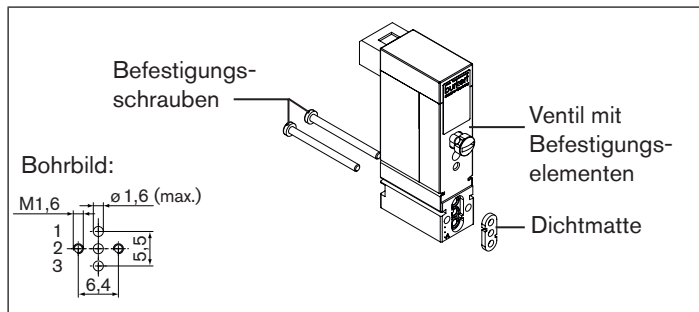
Montagezeichnung für Winkelflansch (FS09)
